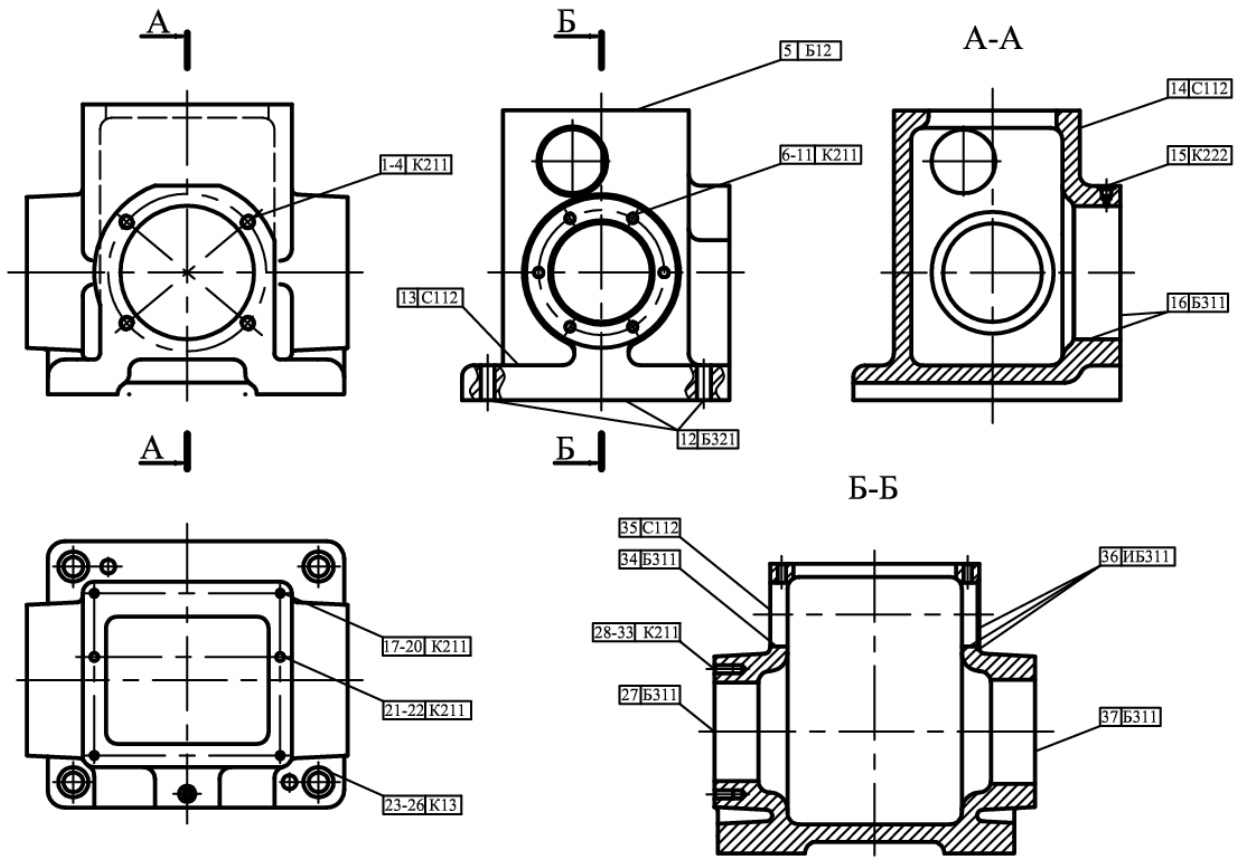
Эскиз детали с нумерацией и обозначением кодов поверхностей
